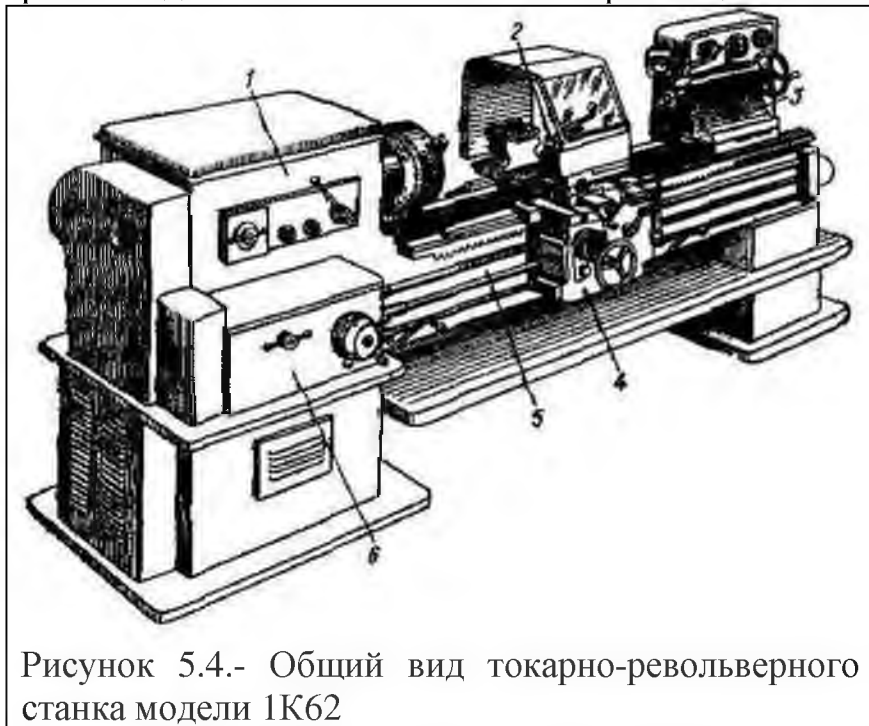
Общий вид токарно-револьверного станка модели 1K62
